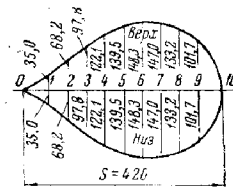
Развертка отверстия в стволе сварного тройника.
